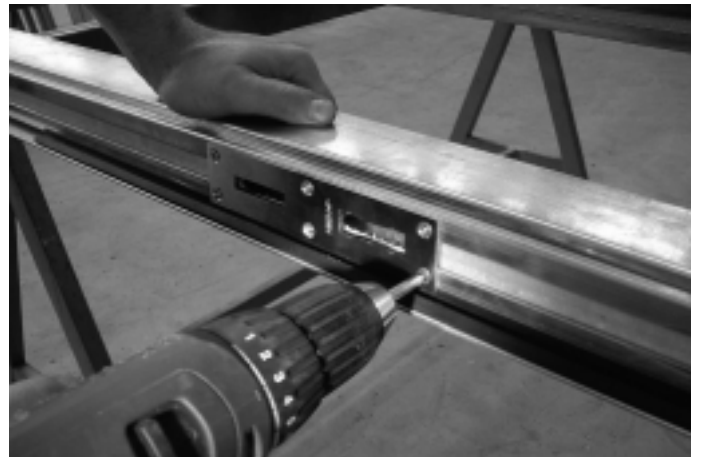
Befestigung Schliessbleche mit Senkschrauben M4x12 (557.046)
